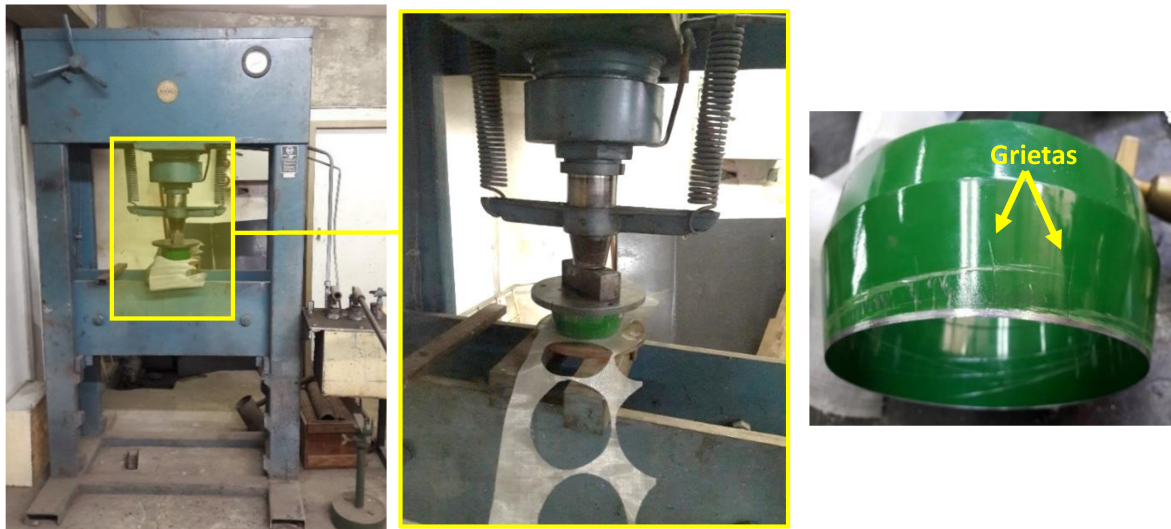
Cortado de las mallas metálicas escala banco (diám. 130 mm).
